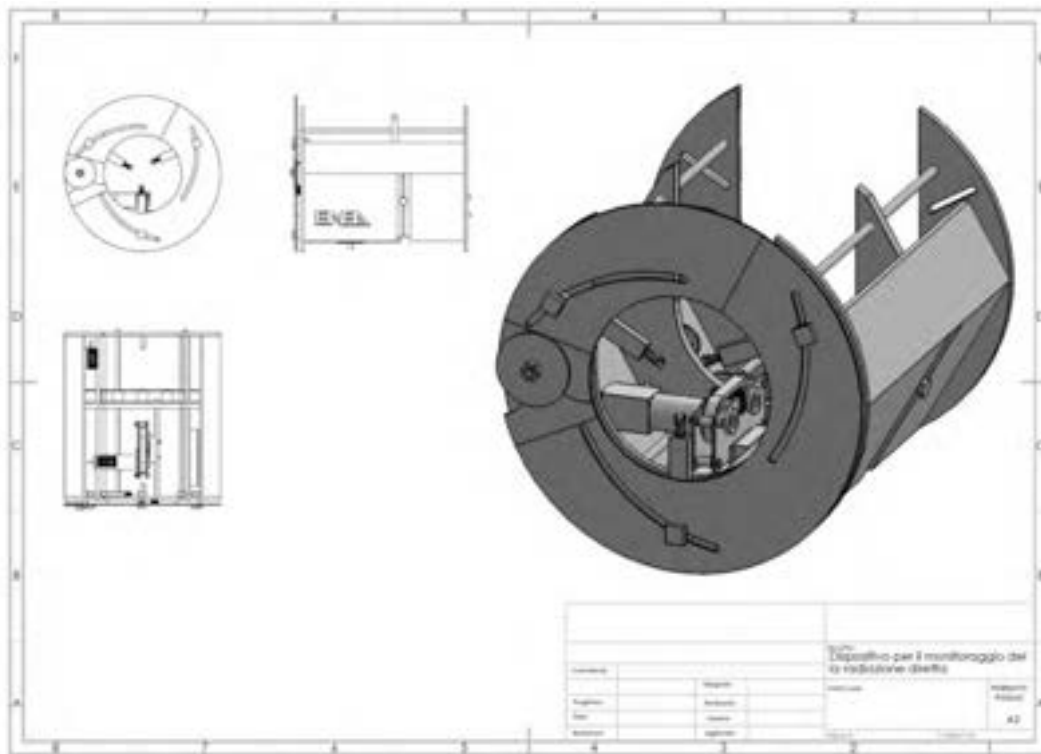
Vista assonometrica del dispositivo di misura e relative viste in pianta e sezione
